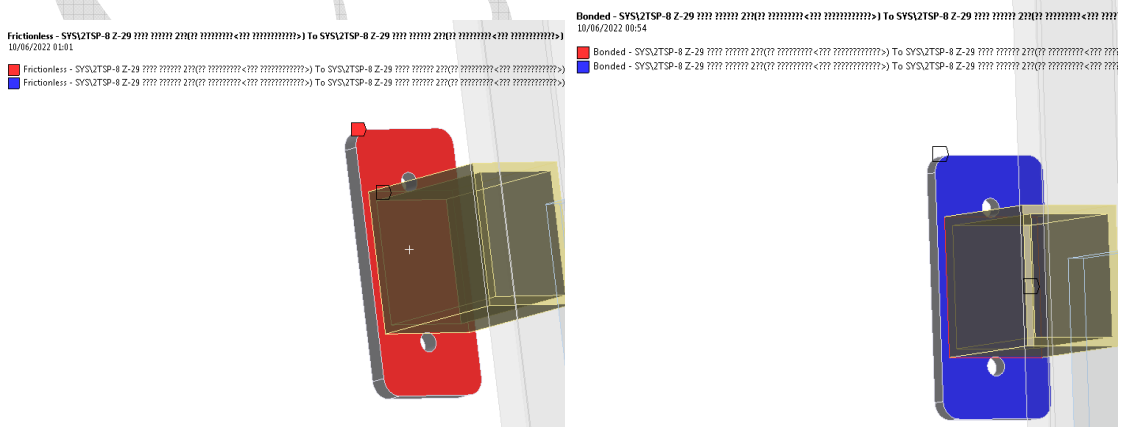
Схема заеріплення деталей за допомогою сварки
